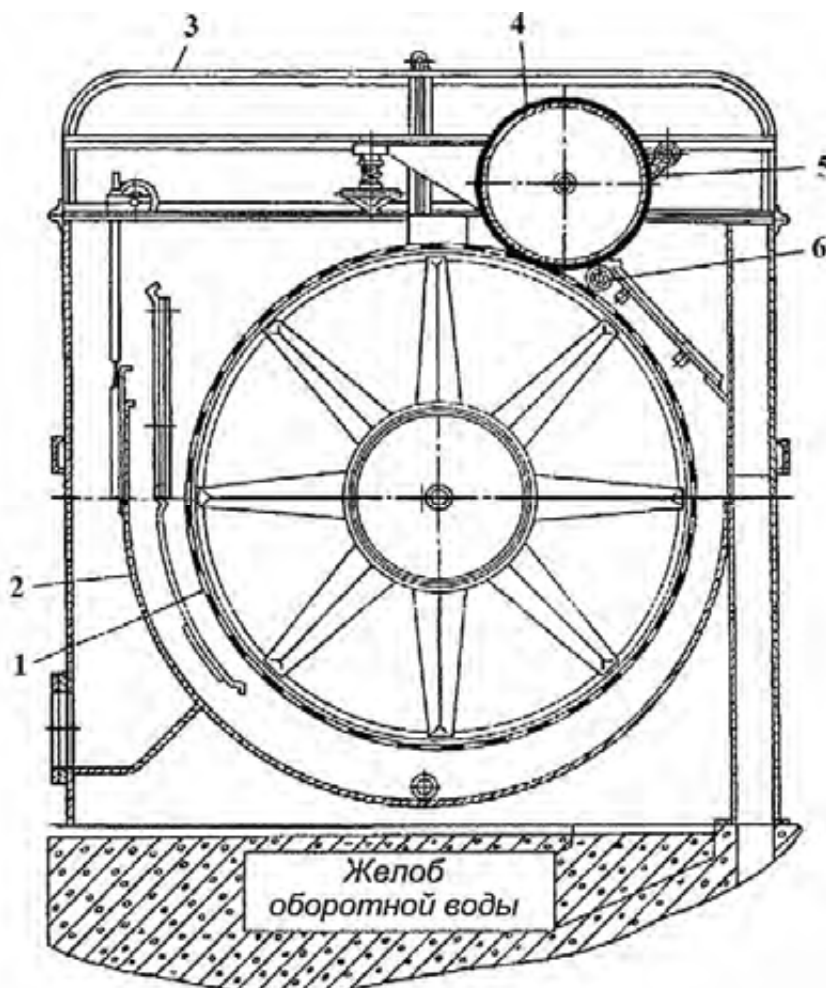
Конструктивная схема шаберного сгустителя типа СШ
